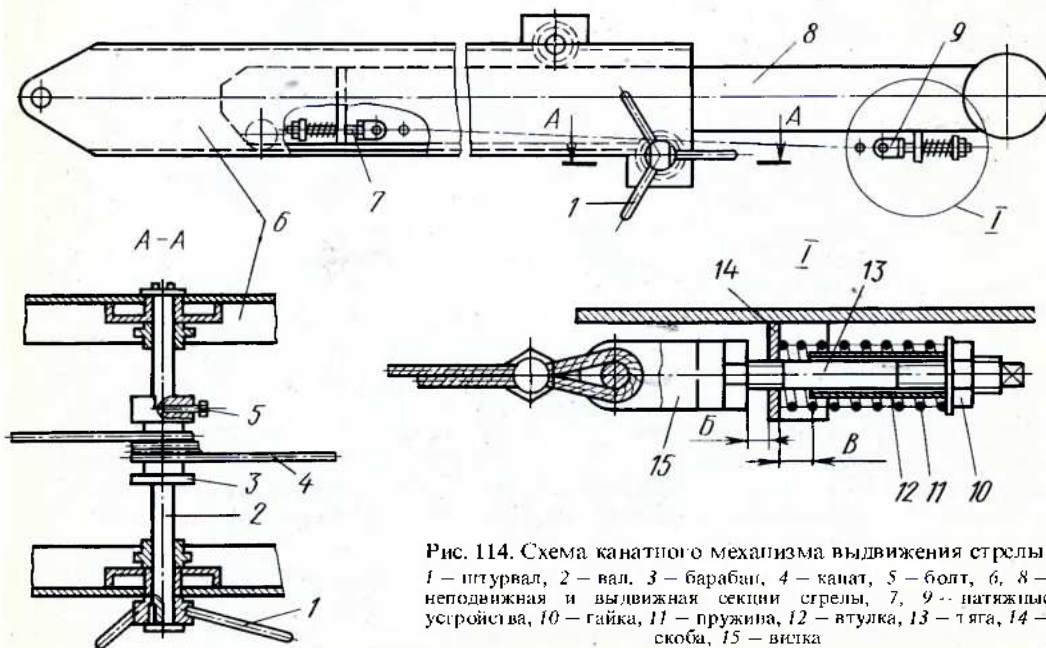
Схема канатного механизма выдвижения стрелы: 1 — штурвал, 2 — вал, 3 — барабан, 4 — канат, 5 — болт, 6, 8 — неподвижная и выдвижная секции стрелы, 7, 9 — натяжные устройства, 10 — гайка, 11 — пружина, 12 — втулка, 13 — тяга, 14 — скоба, 15 — вилка
